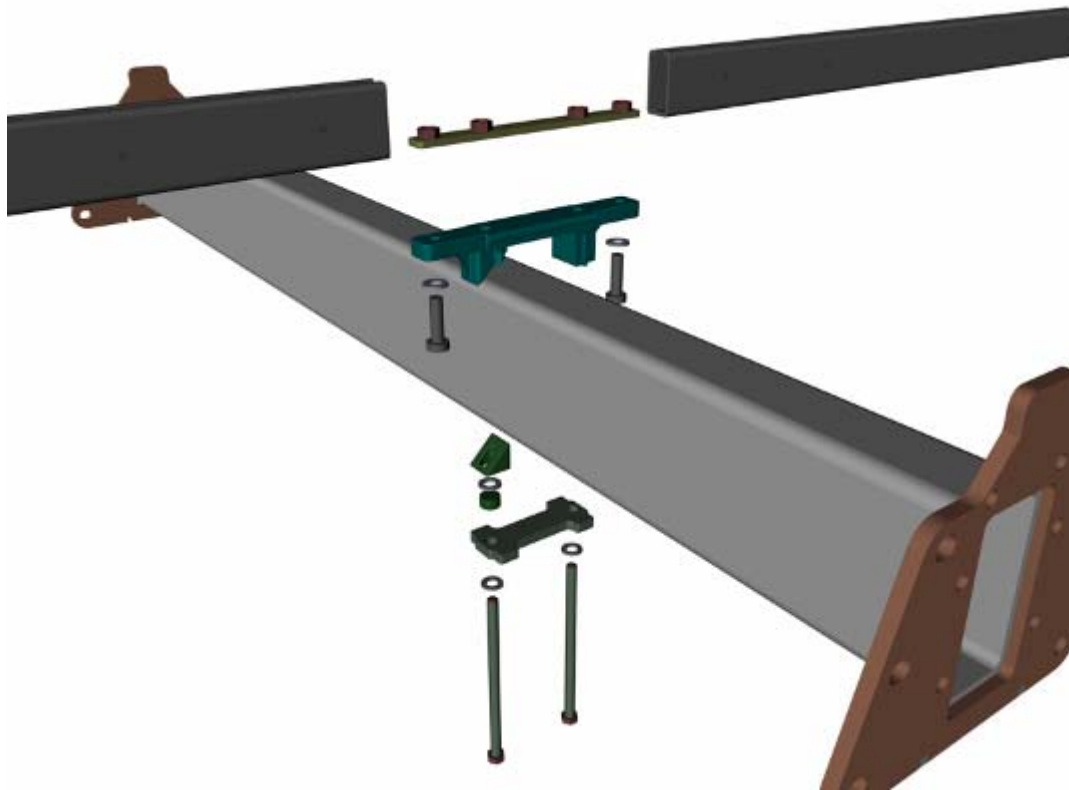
Traversenkonstruktion mit patentiertem Klemmbügel für den Deckaufbau
